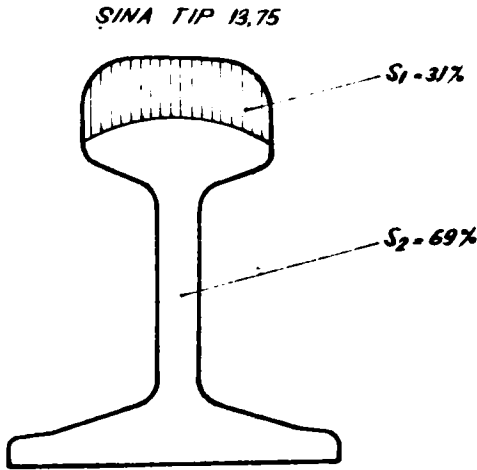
In această figură s-au stabilit suprafețele S_1 placată = 31 % și S_2 de bază 69 %. Determinarea suprafețelor s-a făcut prin planimetrare.
